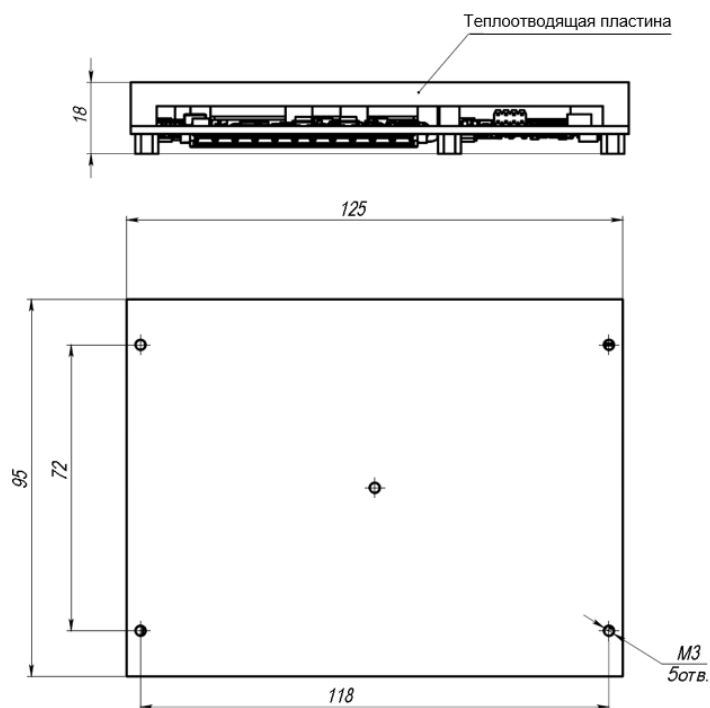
Габаритные размеры изделия (без допусков)
